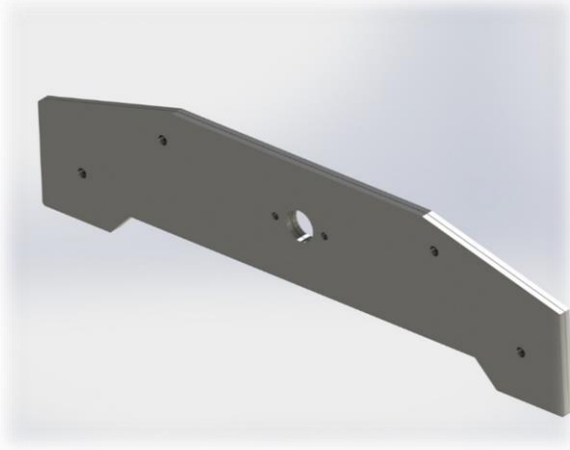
Imagem ilustrativa da condição final de todo processo de usinagem das chapas.
